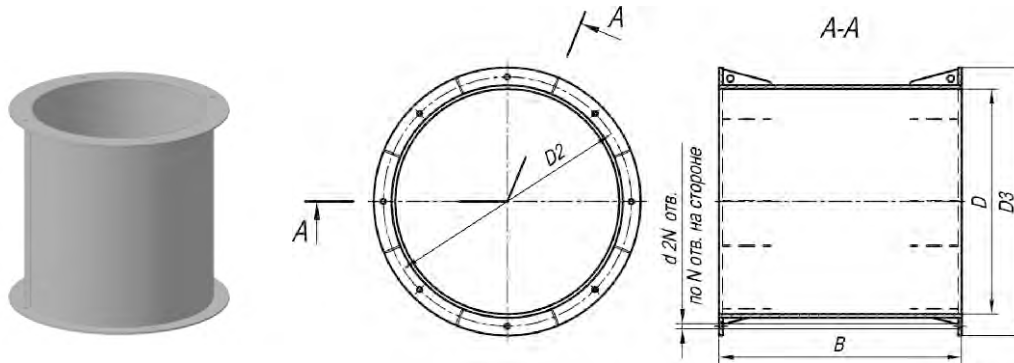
Габаритные и присоединительные размеры стаканов для крышных вентиляторов.
